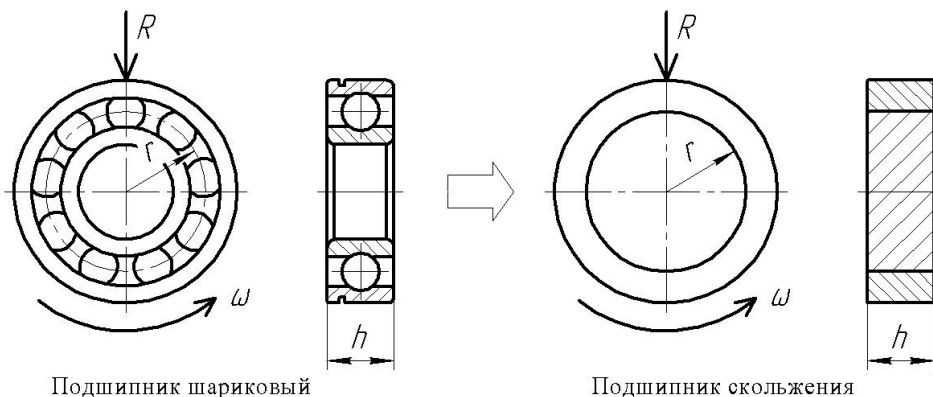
Приведение размеров шарикоподшипника к размерам подшипника скольжения
